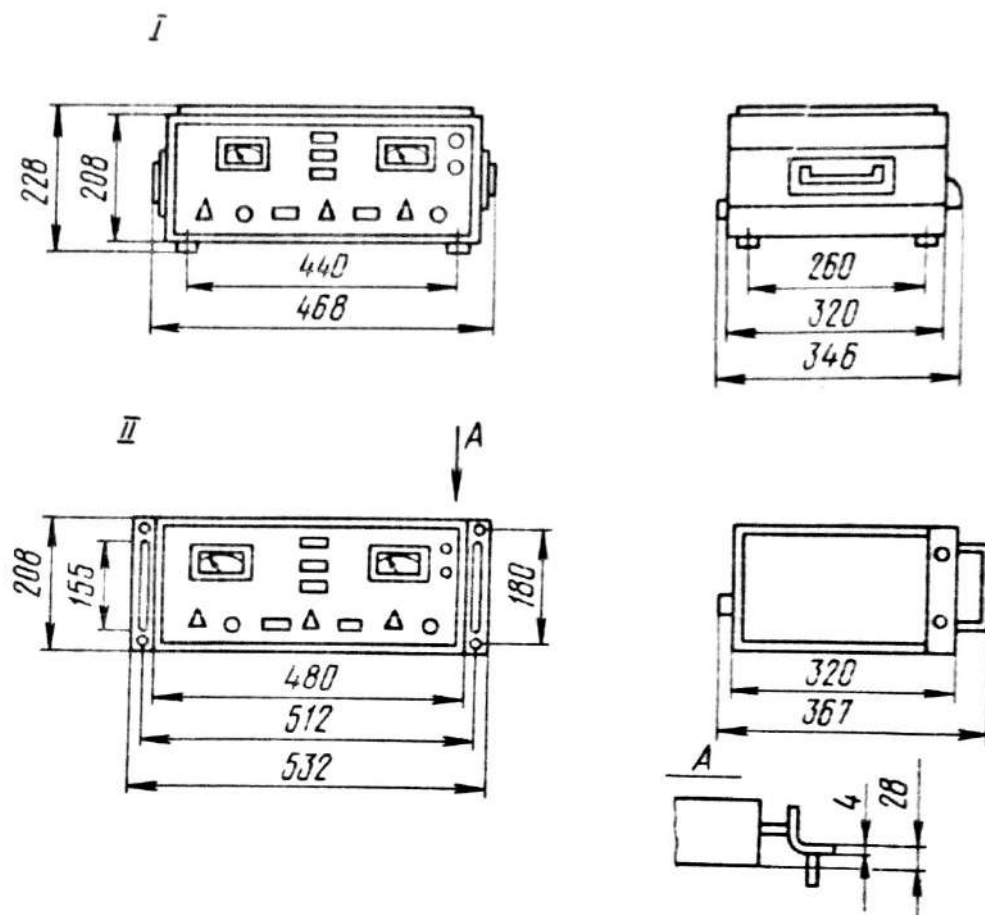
Общий вид измерительного блока вакуумметра ВИТ-3 с габаритными размерами:
